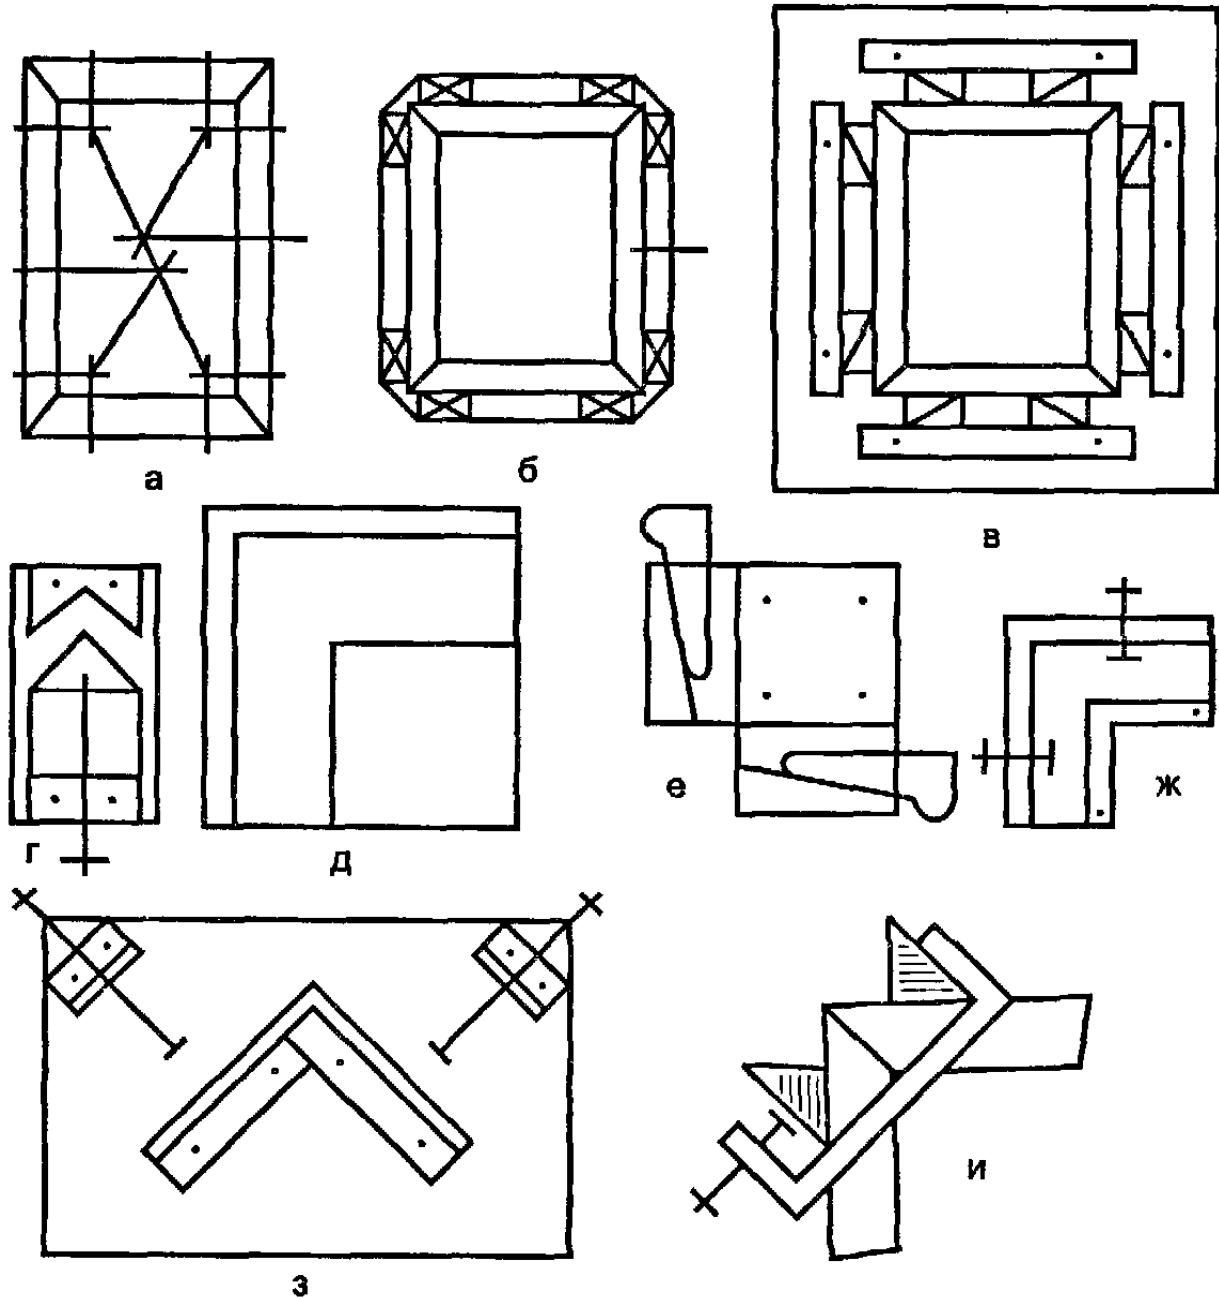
Приспособления для склеивания рамок, коробок, ящиков, обвязок филенчатых щитов (варианты)
